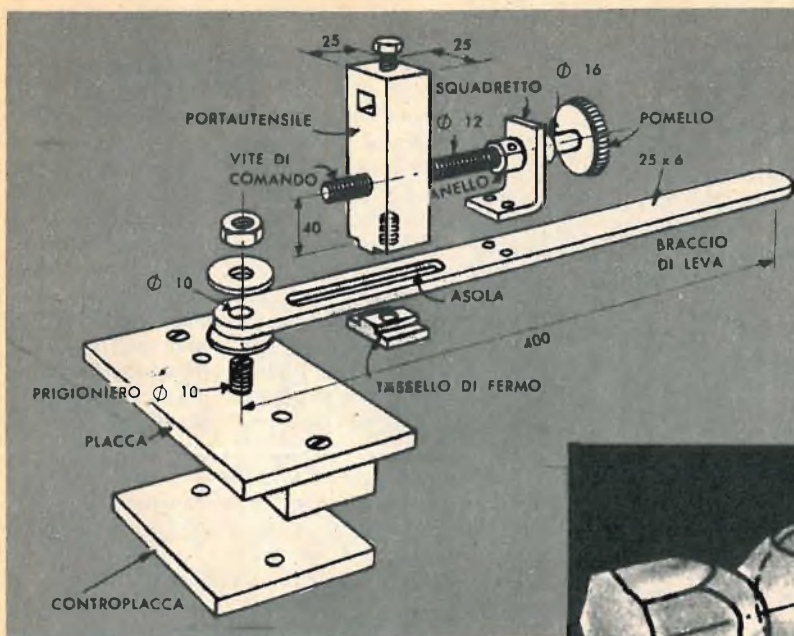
Vista «esplosa» dell'attrezzo. Esso viene montato direttamente sulle guide, se si tratta di un tornio per legno. Trattandosi di un tornio per metalli, conviene effettuare il montaggio sul carrello trasversale.
